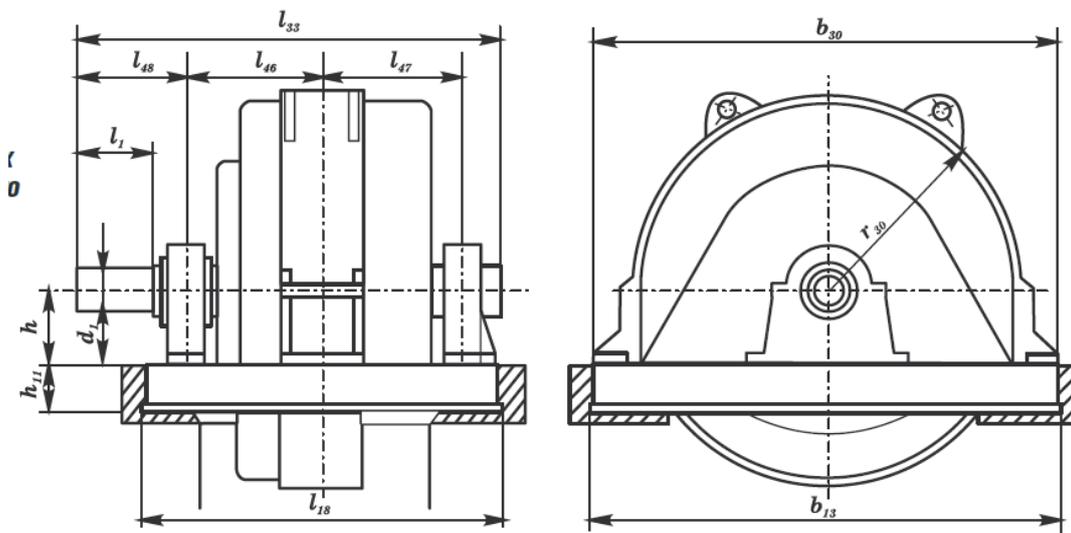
Габаритные, установочные и присоединительные размеры реверсивных двигателей постоянного тока ряда П2 21-25 габаритов
